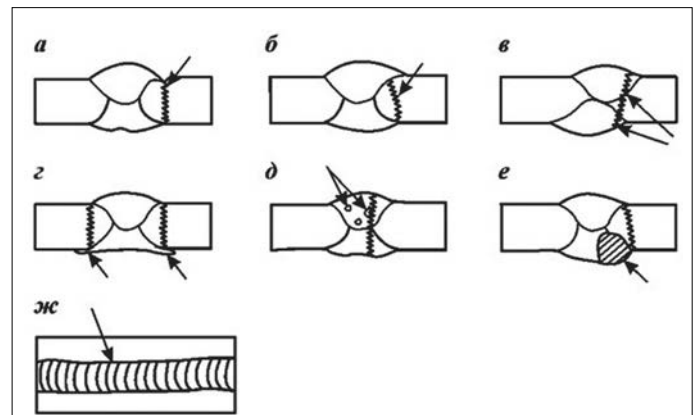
Види дефектів зварних швів і можливий характер їх руйнування: а – подрізи; б – напливи, натіки; в – несплавка зовнішнього й внутрішнього швів через зсув; г – неповне зняття посилення внутрішнього шва з утворенням задривів, уступів; д – пори, шлакові включення на поверхні зламу; е – ділянки ремонтної поверхні заводських швів; ж – нерівномірність параметра зварного шва (ширина й висота посилення)
